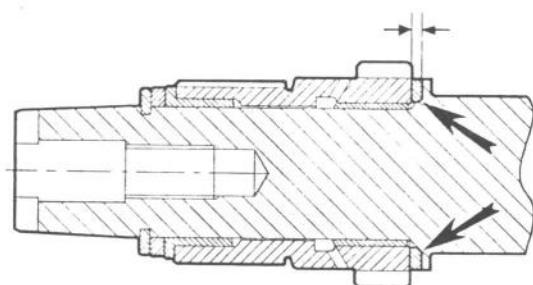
Reglaje del juego en el engranaje del cigüeñal, cuando dicho engranaje va montado sobre casquillos autolubrificantes (en motores construidos posteriormente).
